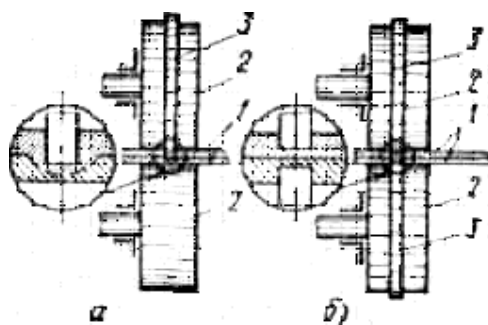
Схема шовной (роликовой) сварки: а – с односторонним деформированием, б – с двусторонним деформированием, 1 – свариваемые детали, 2 – ролики, 3 – рабочие выступы.
